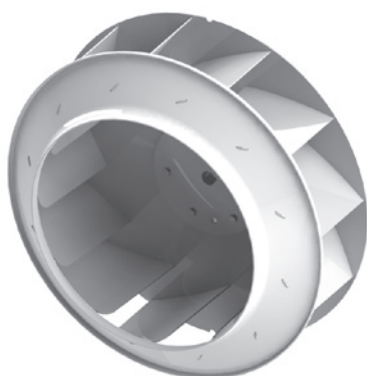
Рабочее колесо ВР 86-77 и VR-86-77
